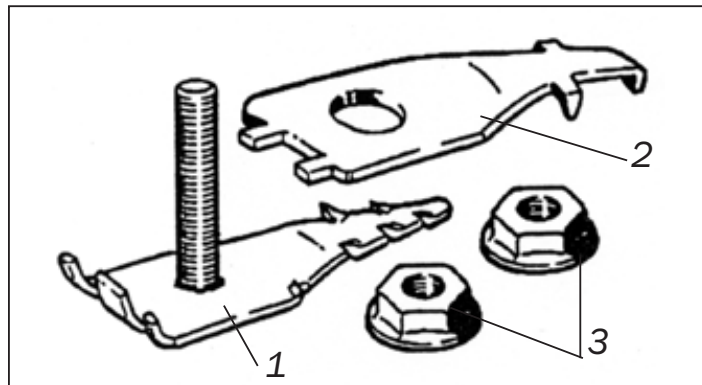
Установка шайбы и гайки крепления штуцера в оголовнике
